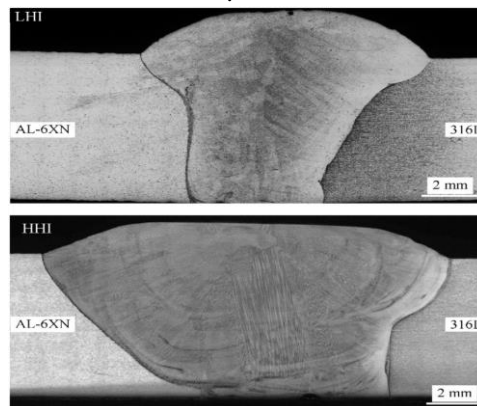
Micrografías de la soldadura disímil AL6XN y 316L
